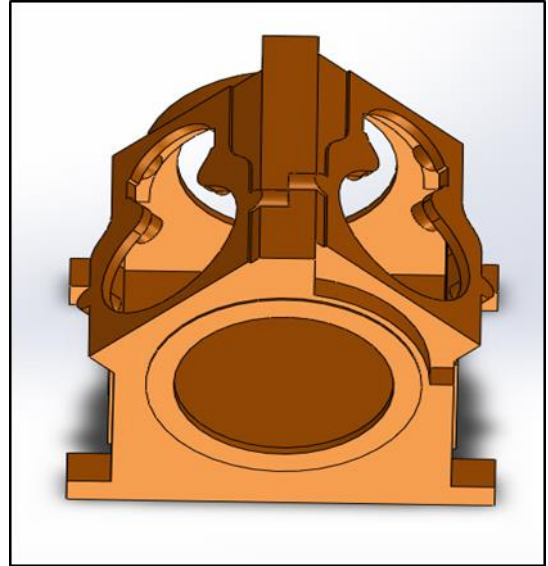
Biyel Kolu Üç Boyutlu Çizimi (Connecting Rod Three-Dimensional Drawing)
